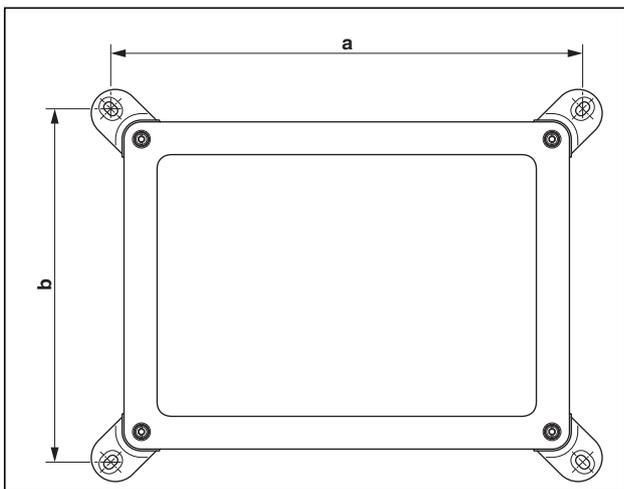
Wandhalterung UCS WM-B..., Bohrplan
